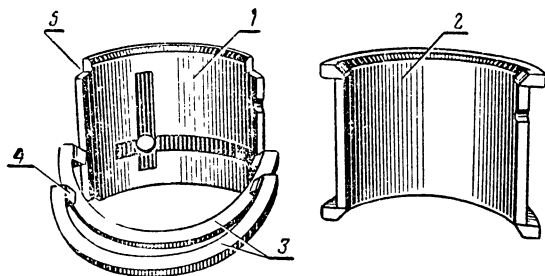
Вкладыши пятого коренного подшипника новой конструкции:
